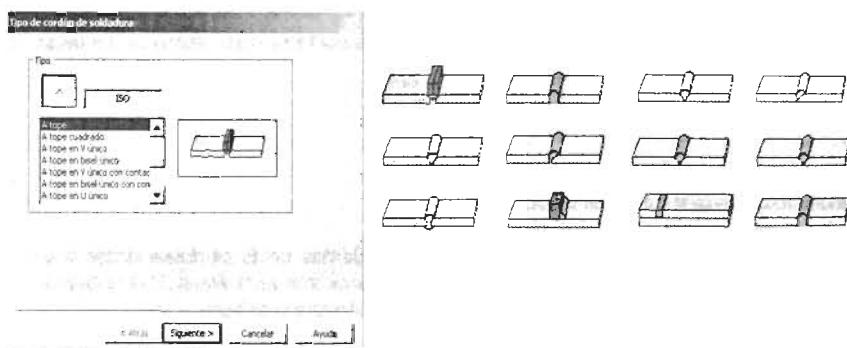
Tipos de Cordones de soldadura.
